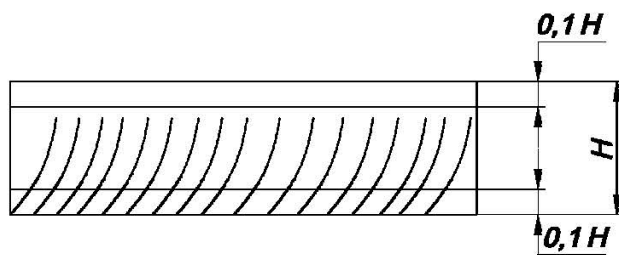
Схема вимірювання обробленої поверхні
